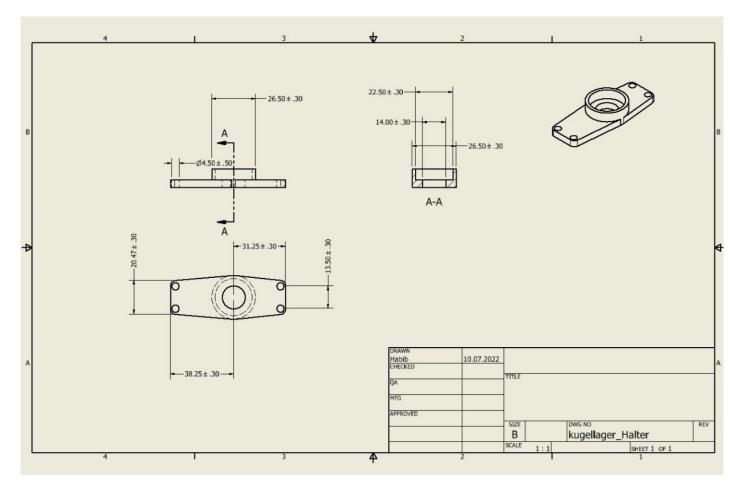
Technische Zeichnung - Kugellagerhalter
